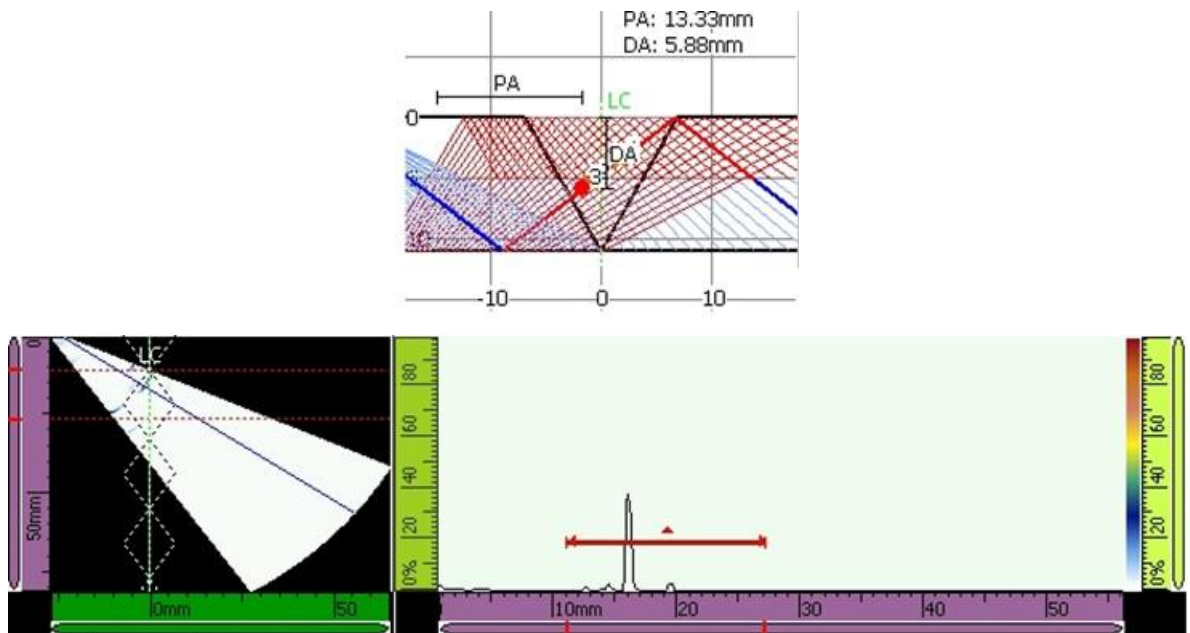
Tubería de inspección de soldadura punto 3.
